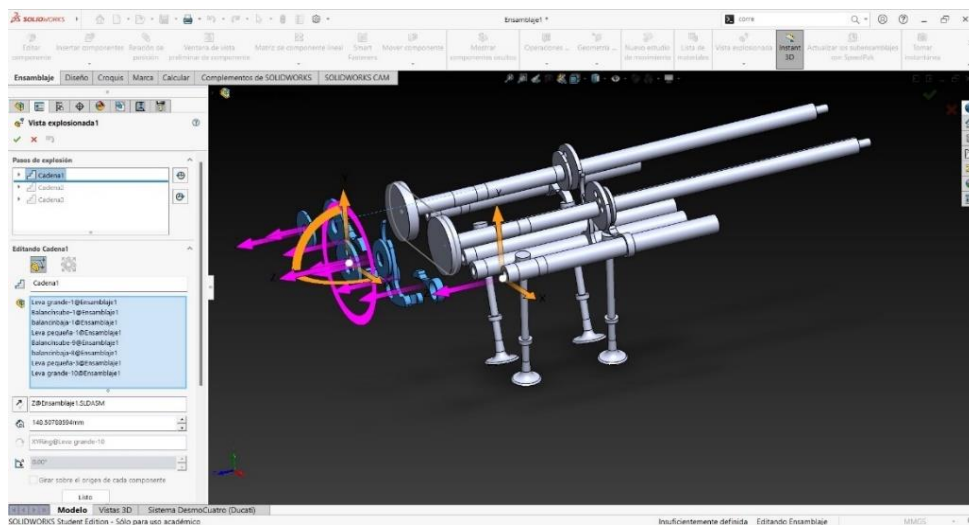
Paso 1 para el explosionado. Fuente: SolidWorks
